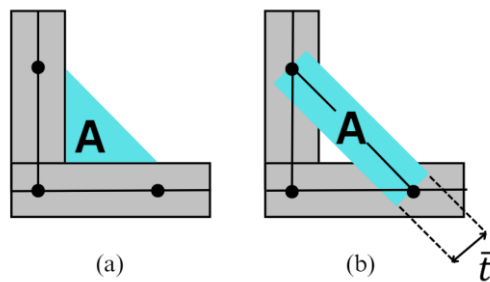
Critério para definição de espessura do elemento representativo da solda para elemento de casca. (a) Cordão de solda real. (b) Representação do cordão de solda por elemento de casca oblíquo.
